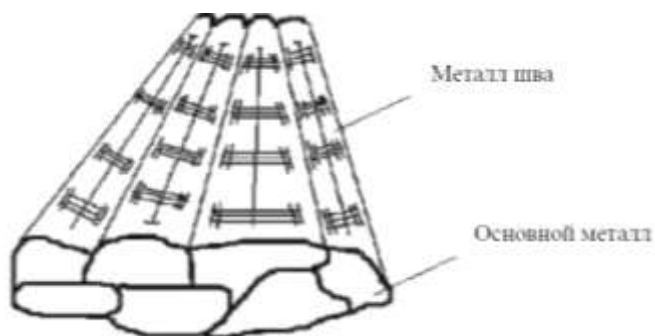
Схема роста кристаллов от границы сплавления в сварочной ванне
